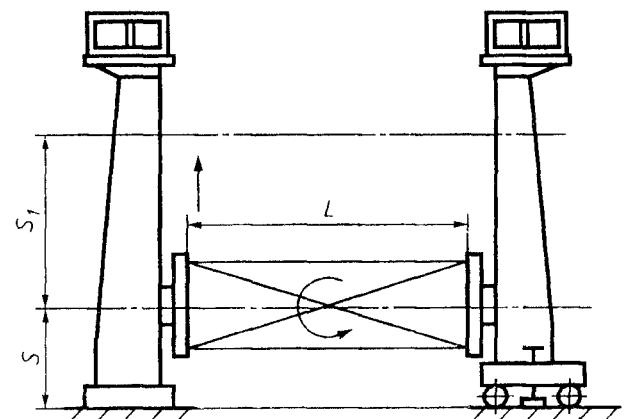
Кантователь центровой двухстоечный с подъемными центрами
